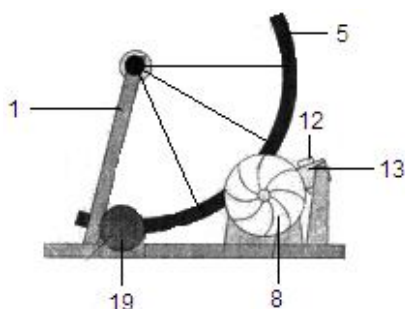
Вид регулирующего устройства со стороны крыльчатки вентилятора
